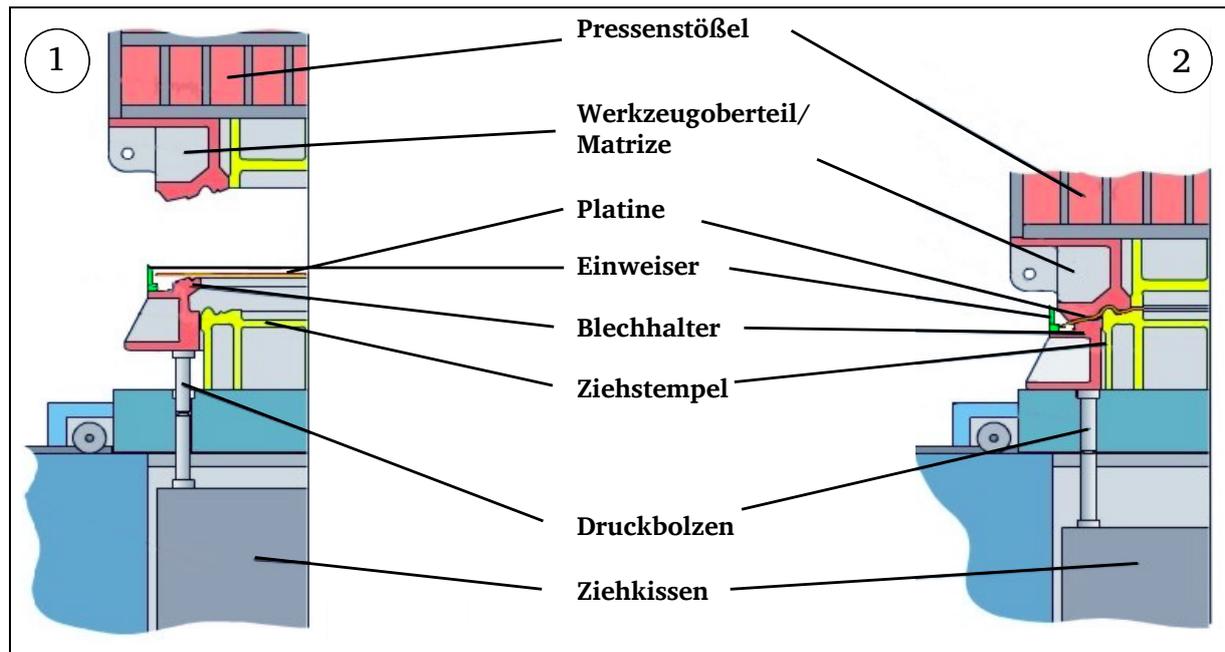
Prinzipieller Aufbau eines Ziehwerkzeuges [Mül07]
